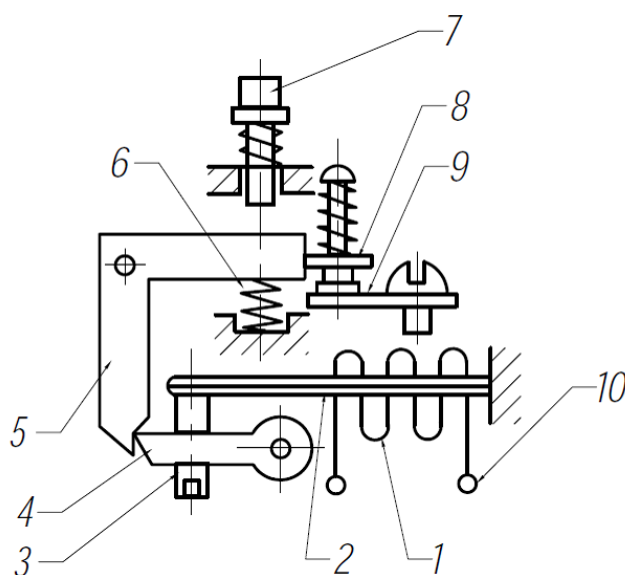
Теплове реле ТРН: 1 – нагрівач; 2 – біметалева пластина; 3 – регулювальний гвинт; 4 – защіпка; 5 – важіль; 6 – пружина; 7 – кнопка повернення; 8 – рухомий контакт; 9 – нерухомий контакт; 10 – вивід нагрівача
